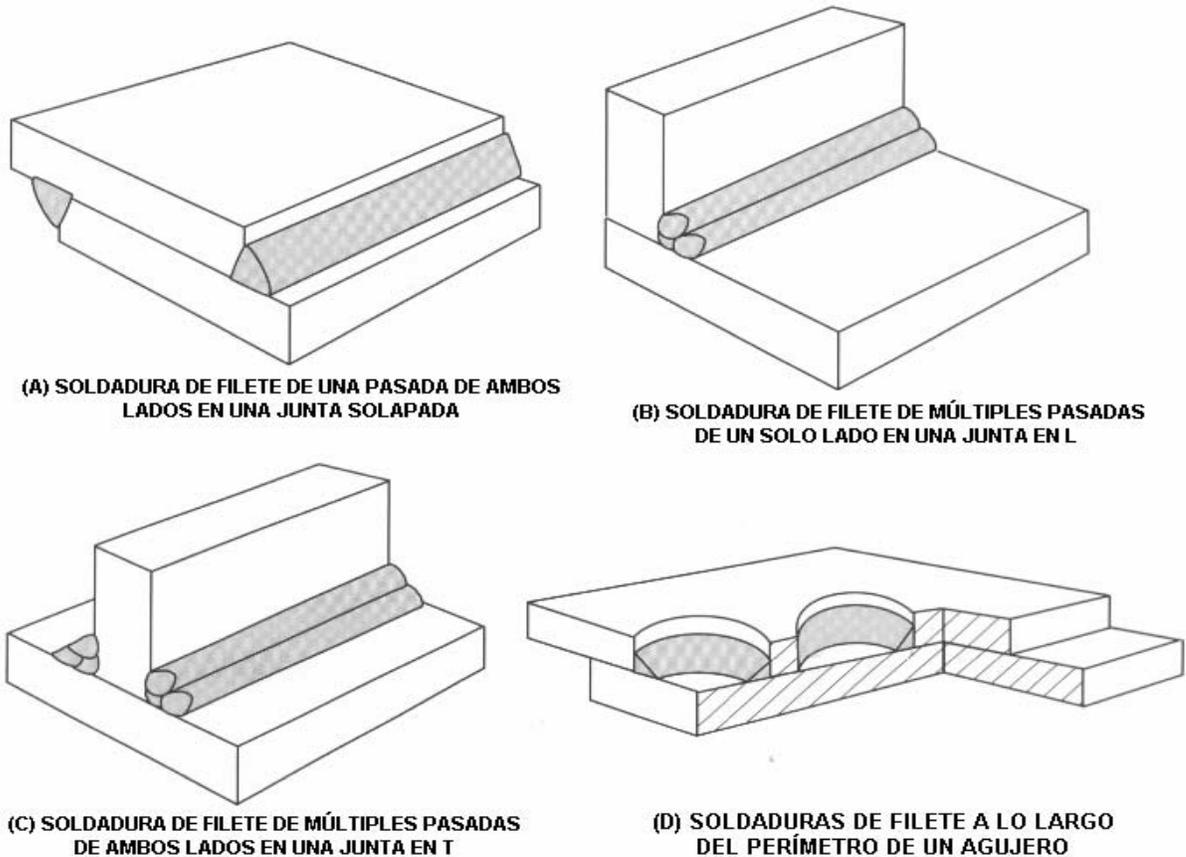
Aplicaciones de la soldadura de filete
